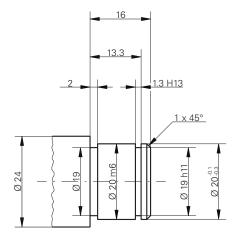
Peça de trabalho de exemplo - Desenho Técnico
